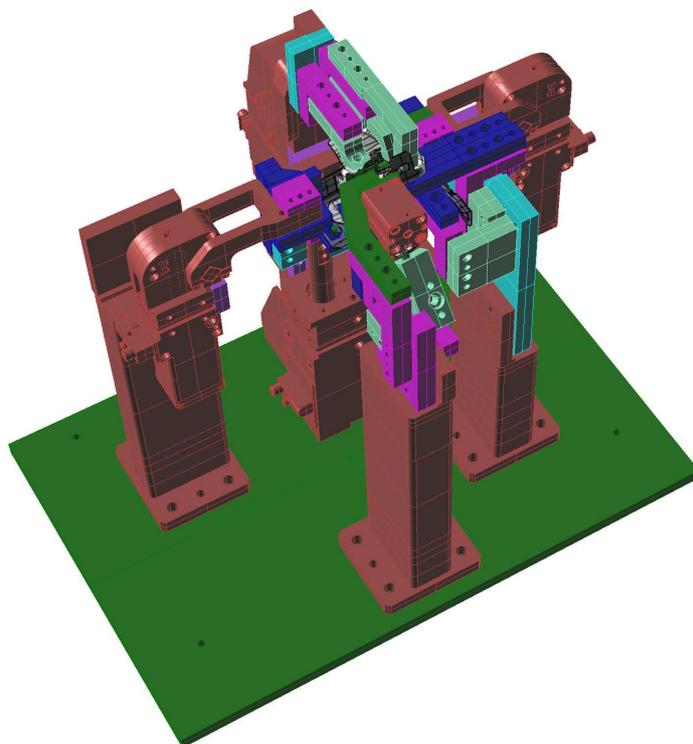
Attrezzatura di geometria OP.10 DX
